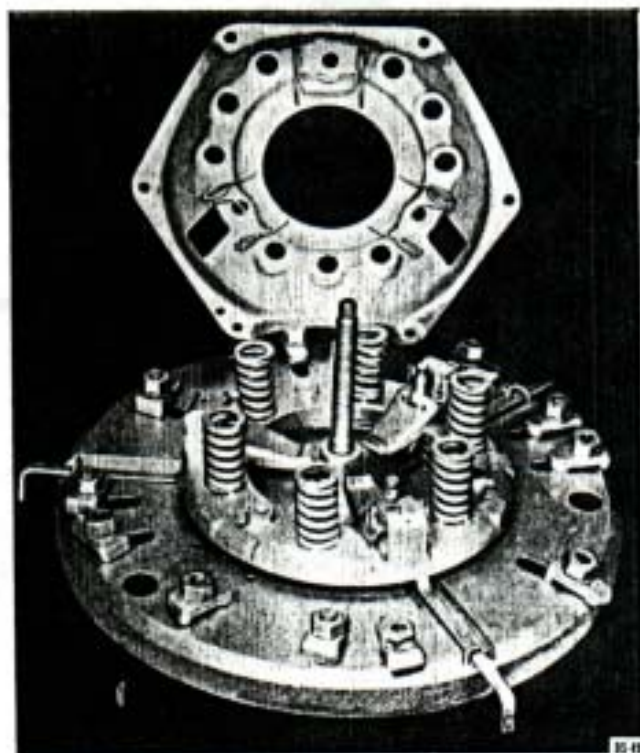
Correcta disposición del conjunto del embrague sobre la herramienta HS-64; previa al ajuste de la placa de presión.
